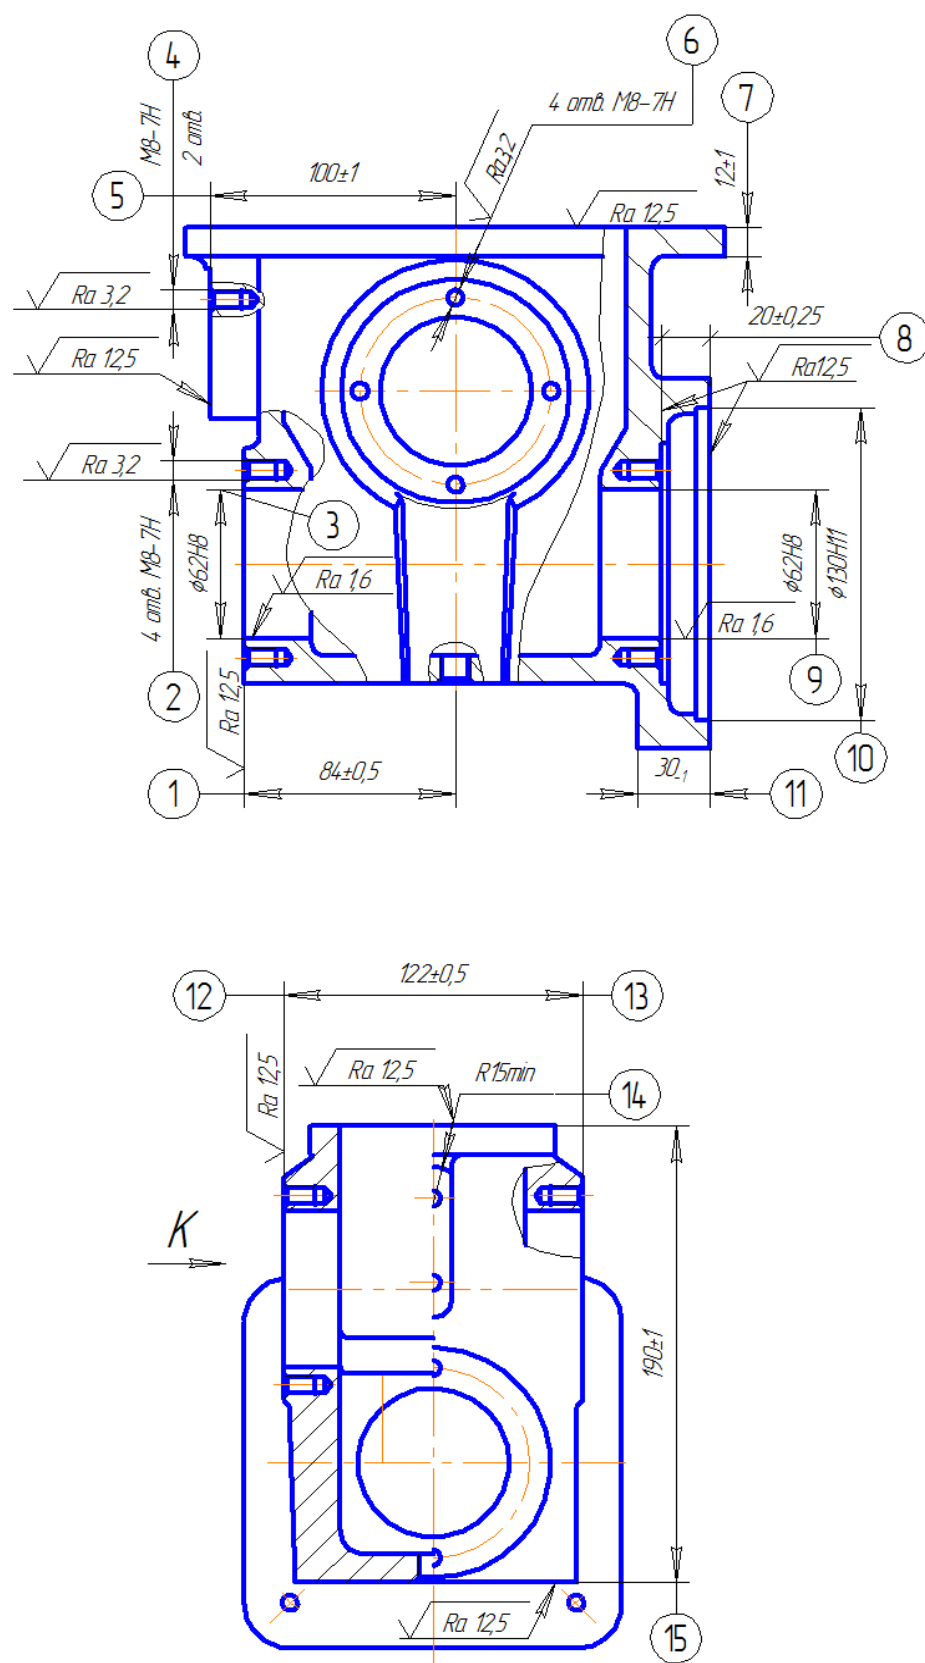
Эскиз детали «Корпус редуктора водяной помпы»
